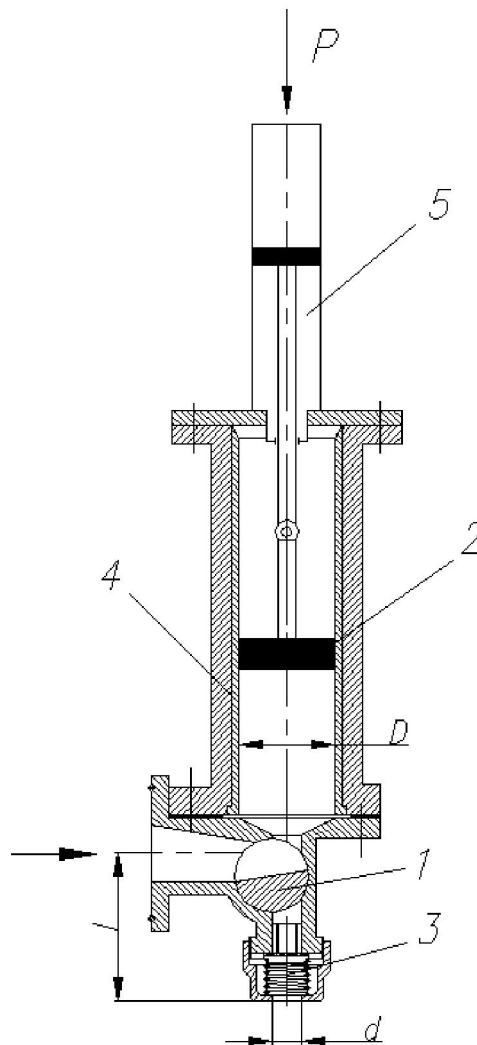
Схема до розрахунку дозатора: 1 - поворотний кран; 2 - поршень; 3 - насадка; 4 - мірний циліндр; 5 - пневмоциліндр.
